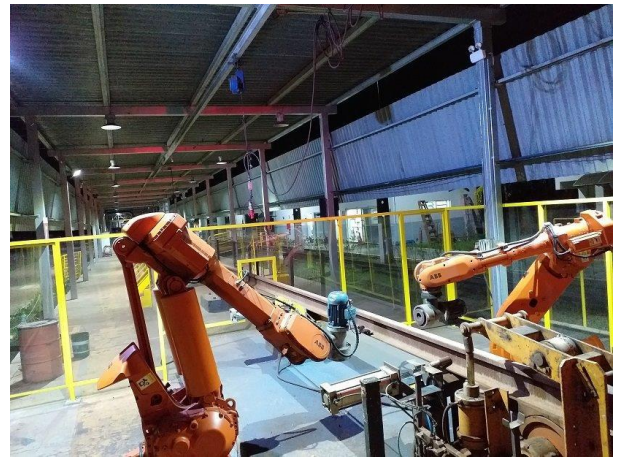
Robô manipulador para esmerilhamento de trilho pós solda
